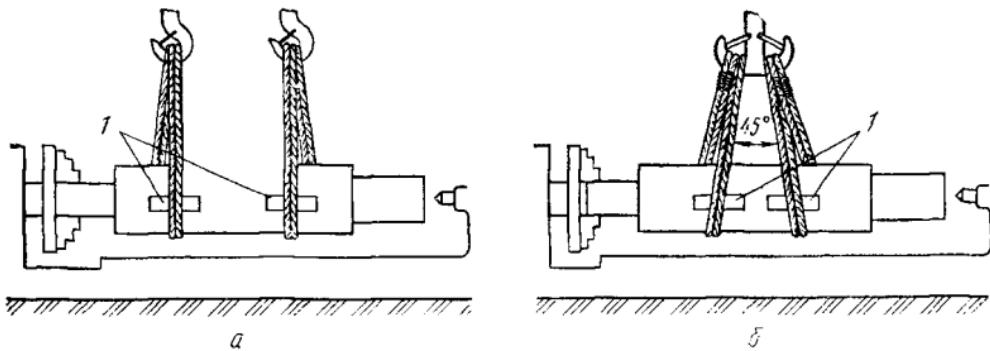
Строповки обработанных валов для их транспортирования и установки на станки:
